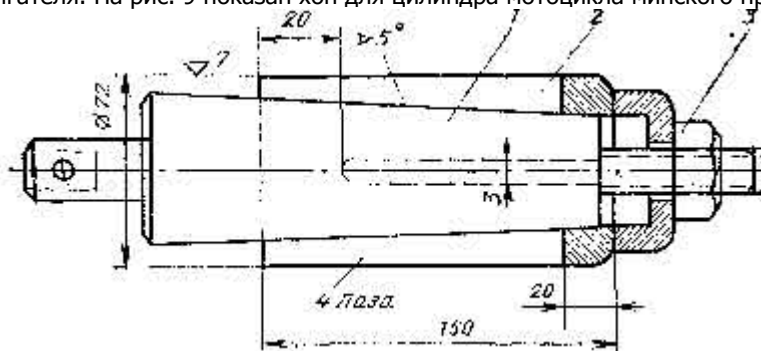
Притир для цилиндра двигателя «Иж-Планета»: 1—корпус Притира; 2—разрезная втулка; 3—гайка
